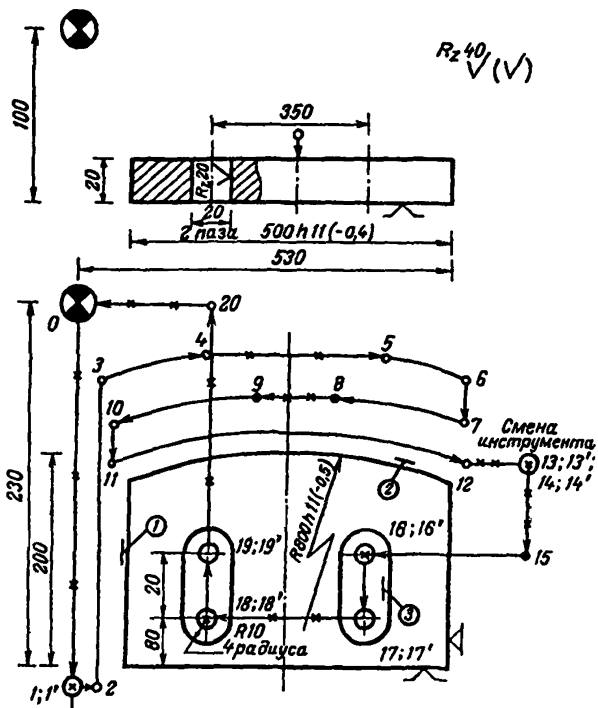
Эскиз детали для примера нормирования операции контурного фрезерования.
